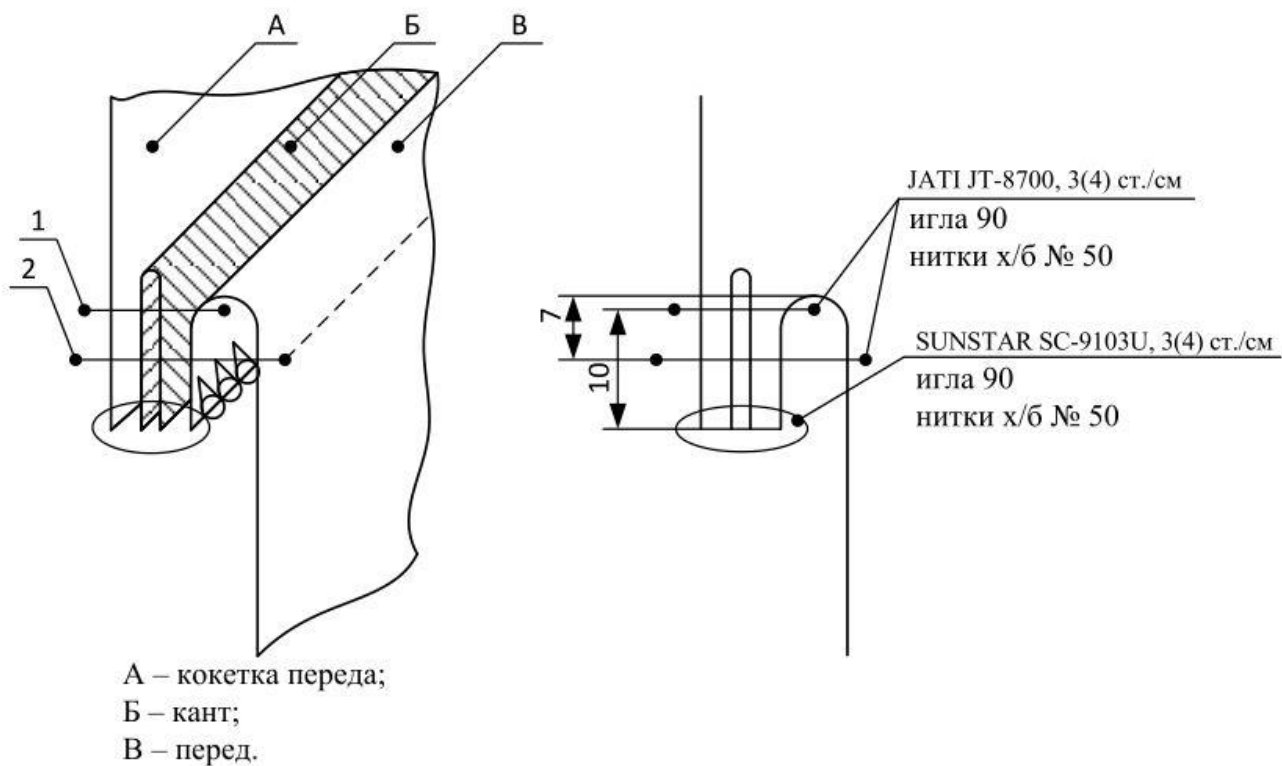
Схема обработки поперечных швов соединения переда блузона
